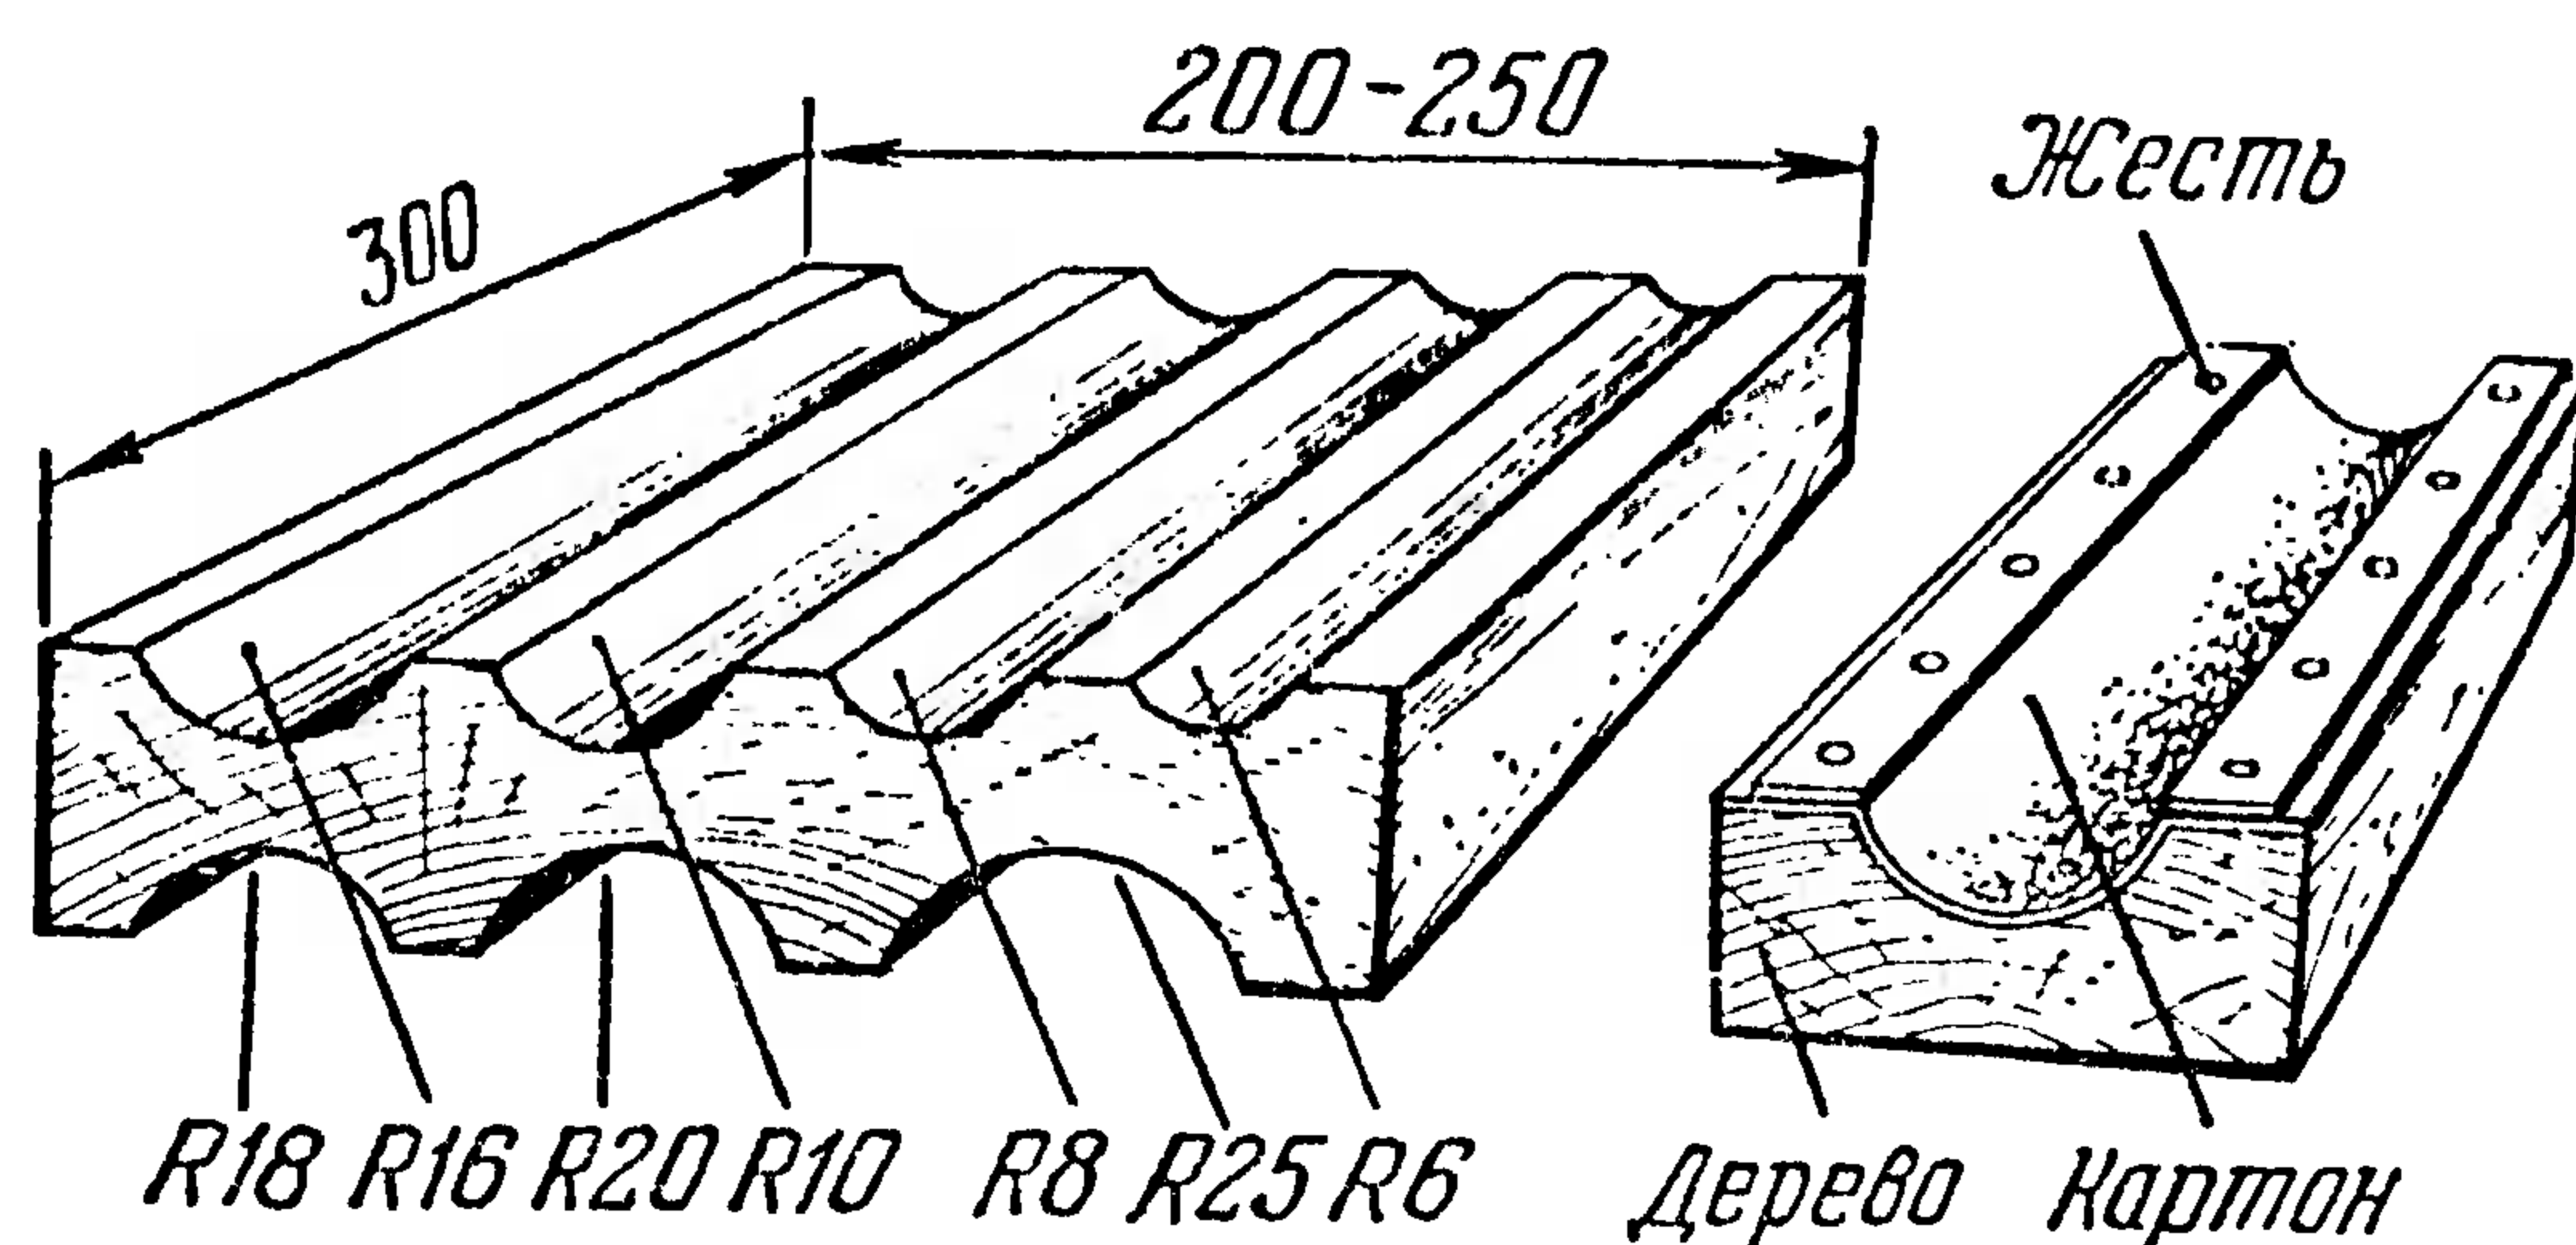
Приспособление для кругления корешков книжных блоков, скрепляемых бесшвейным способом.
